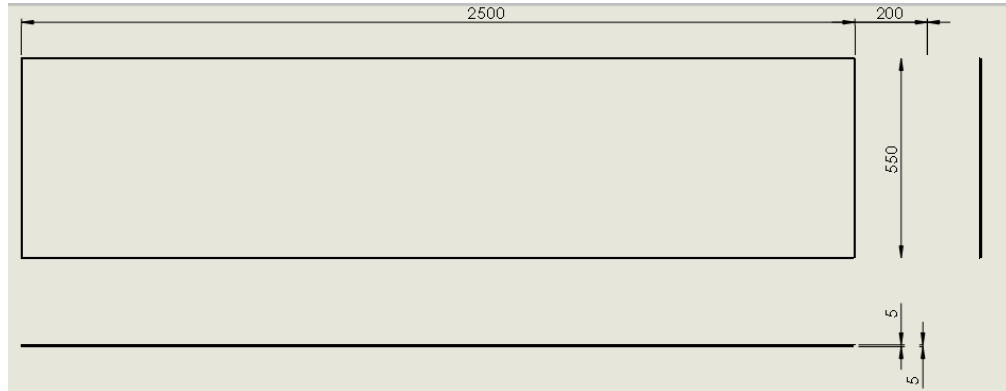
Plano de Construcción Tabla de Madera (mm).
